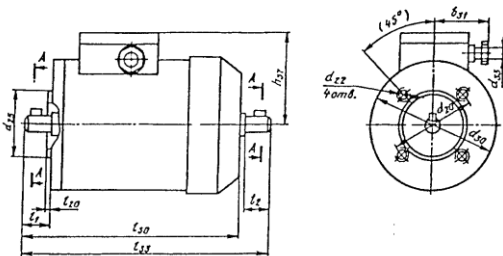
Габаритные, установочные и присоединительные размеры двигателей исполнений 1М3681, 1М3682
